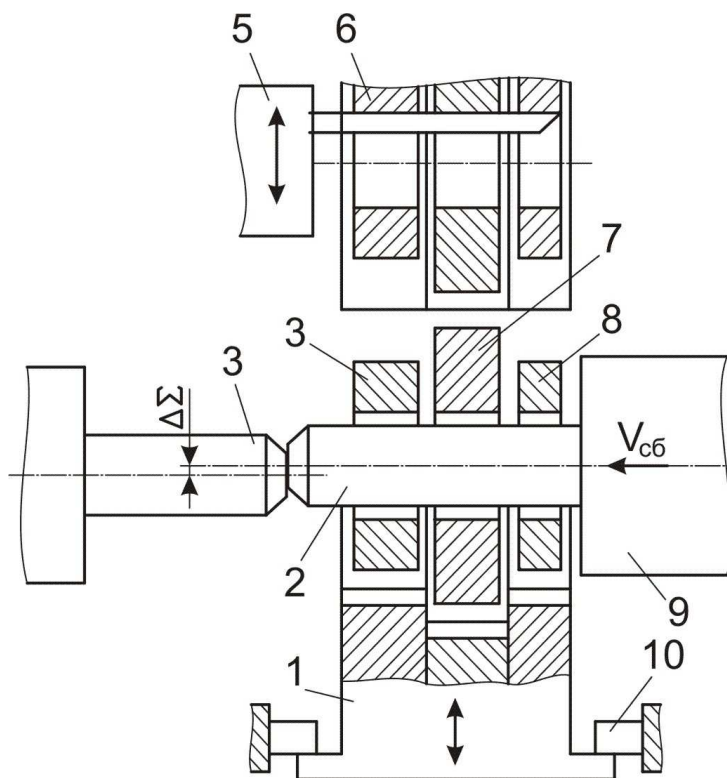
Схемы сборочного механизма для одновременной сборки группы деталей [4]:
